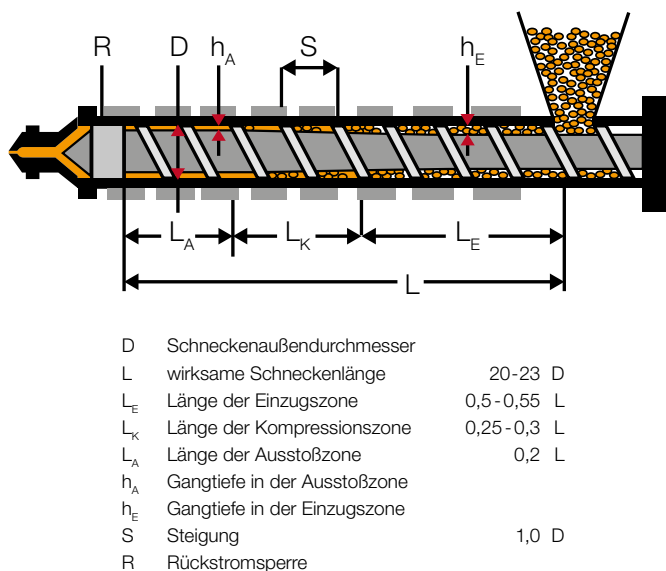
Schnecken geometrie; Begriffe und Maße von Dreizonenschnecken für Spritzgießmaschinen
